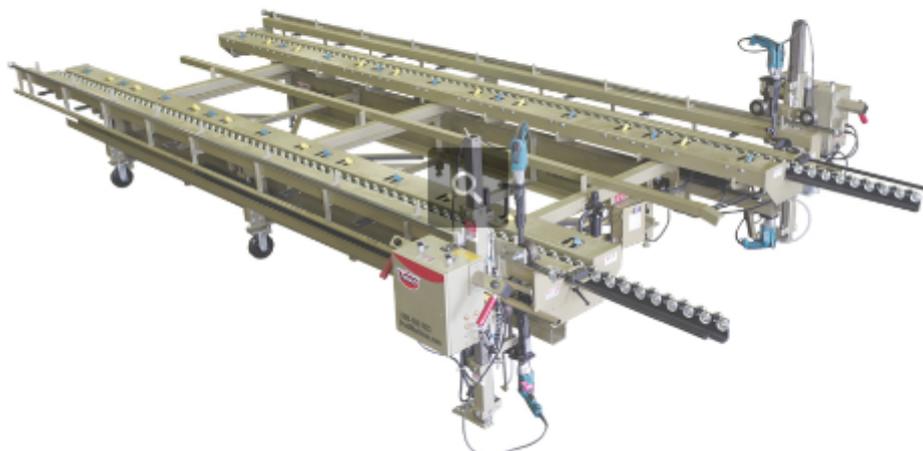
Mesa de panelizado Triad Steel Stud Framing Table.
